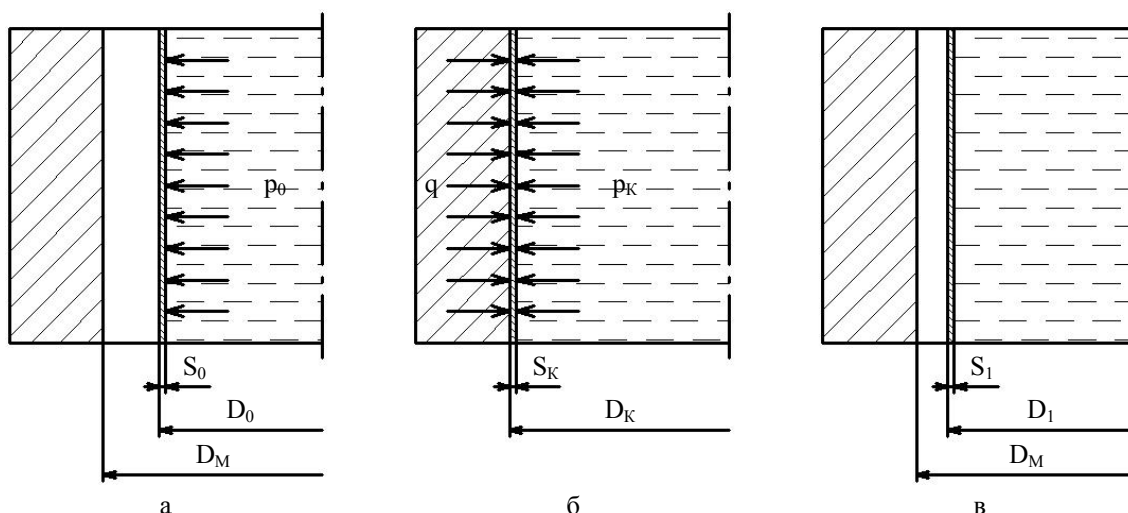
Этапы контакта заготовки с поверхностью матрицы:
